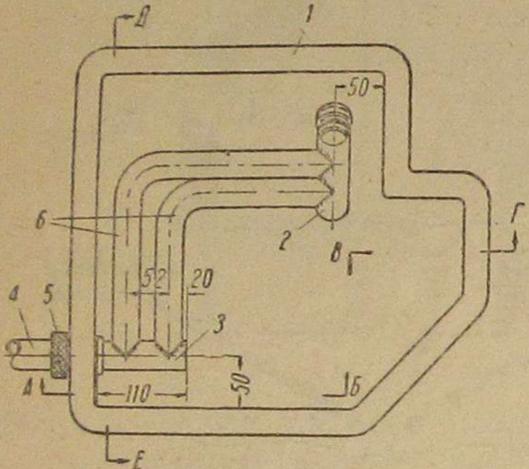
Маслоподогреватель для двигателя трактора СГ-60:
